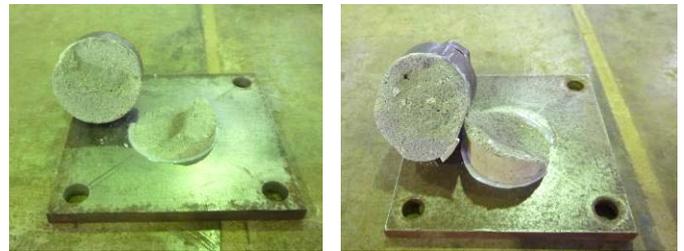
破壊状況 (左: 厚さ 10 mm、右: 厚さ 30 mm)
